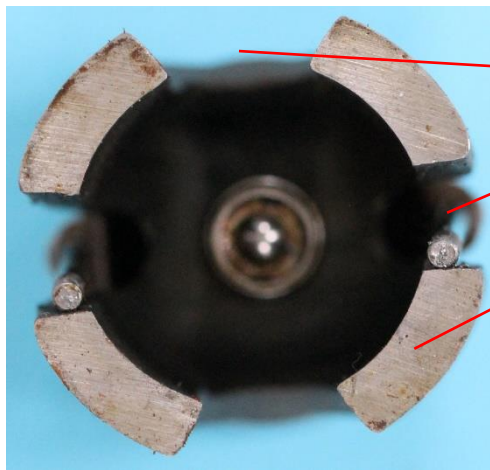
Befestigung des vierpoligen Tulpenmagneten Mit Spannbolzen und Spannstege
